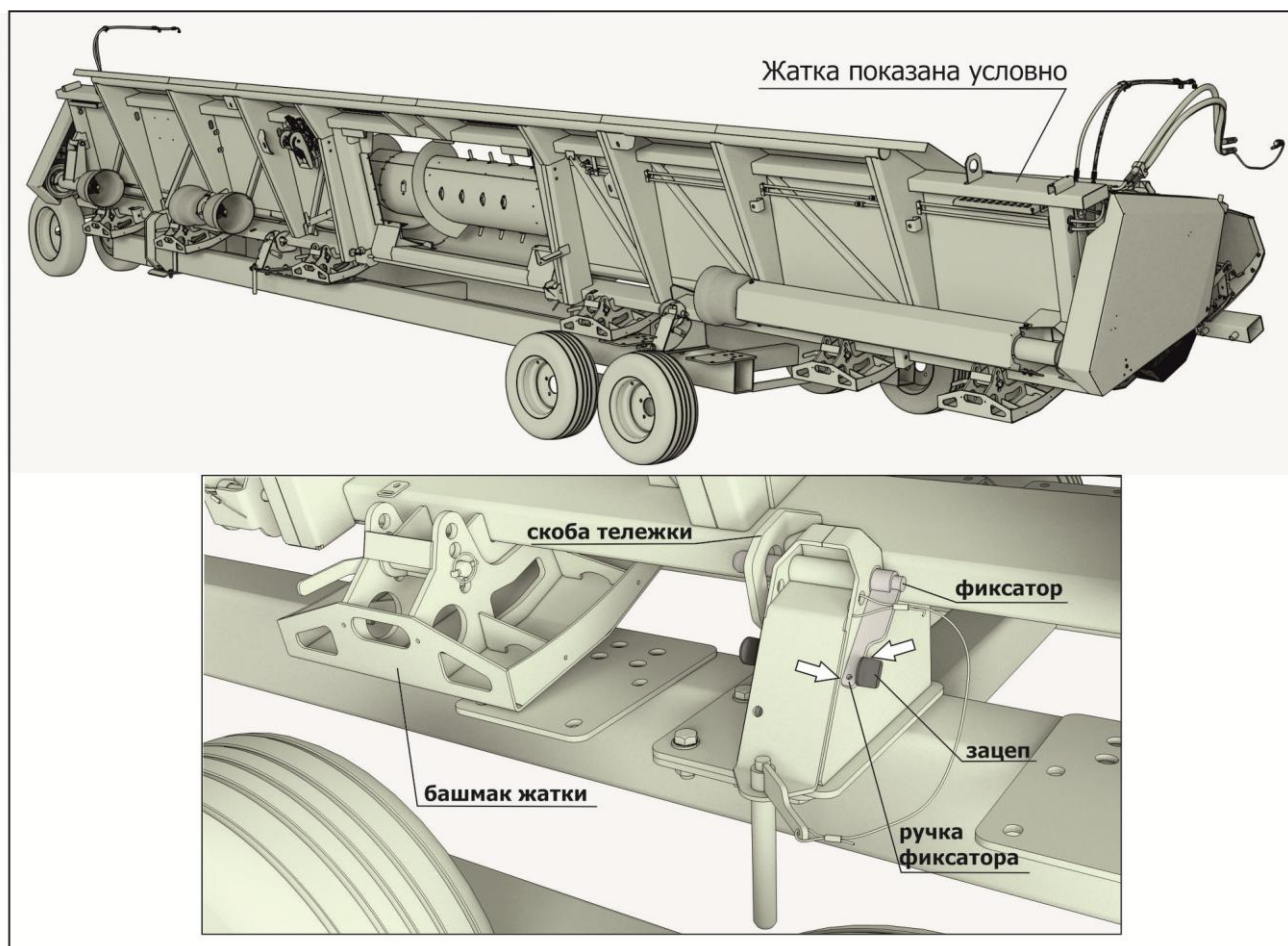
Установка жатки на приспособление ППА-4000
